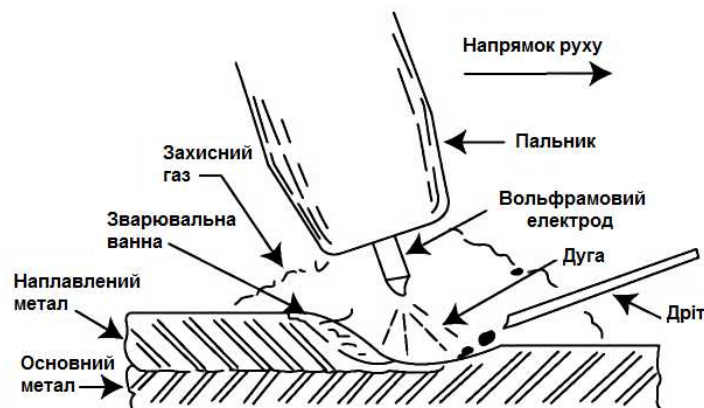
Схема GTAW-процесу наплавлення [25]
